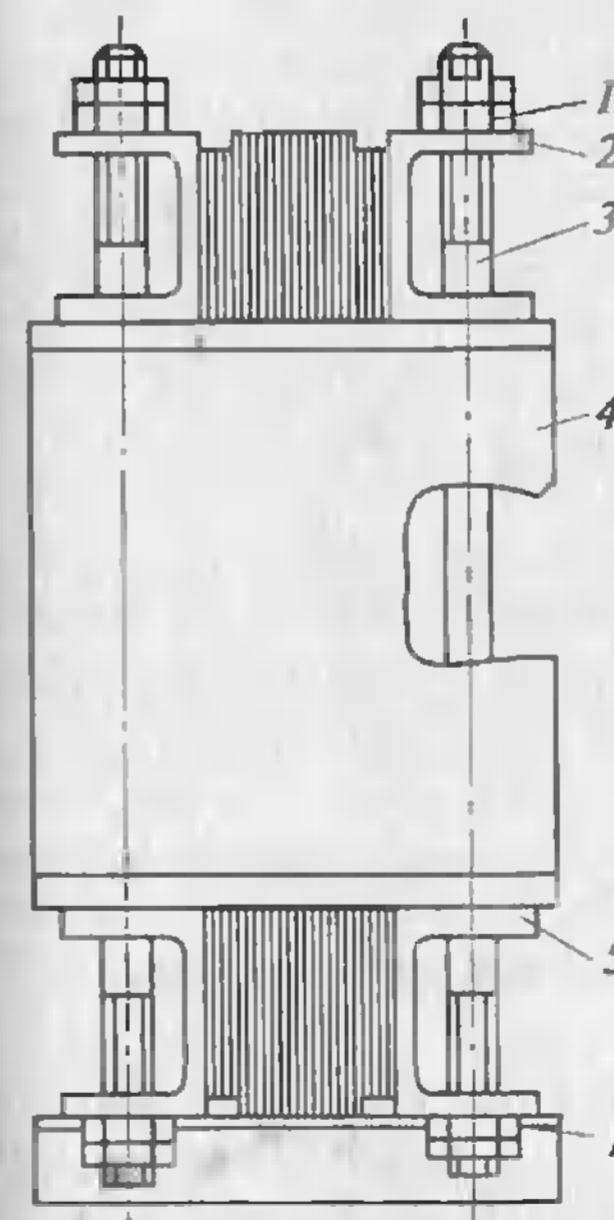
Подпрессовка обмоток трансформатора ярмовыми балками:
